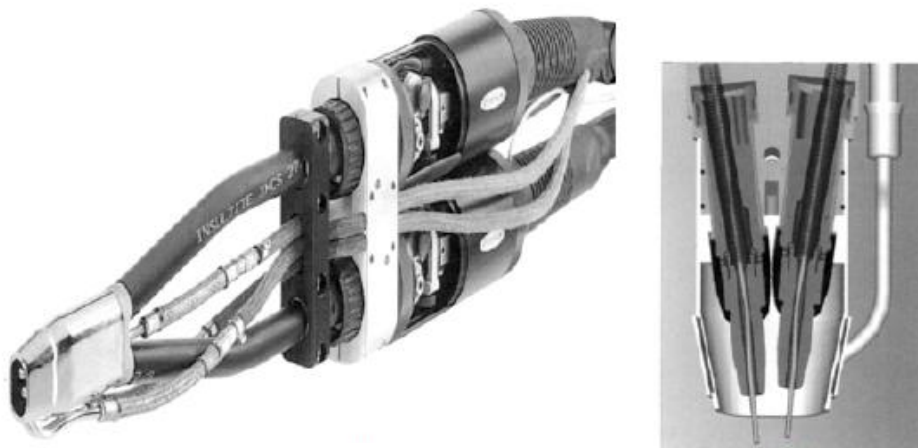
Ejemplo de antorcha de soldadura Tándem. (3)
